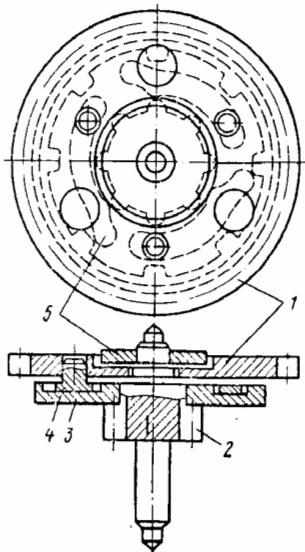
Схема устройства муфты свободного хода часов с автоматическим подзаводом пружины: 1 — колесо реверсивное; 2 — триб реверсивного колеса; 3 — чашка реверсивной муфты; 4 — собачки; 5 — шайба
